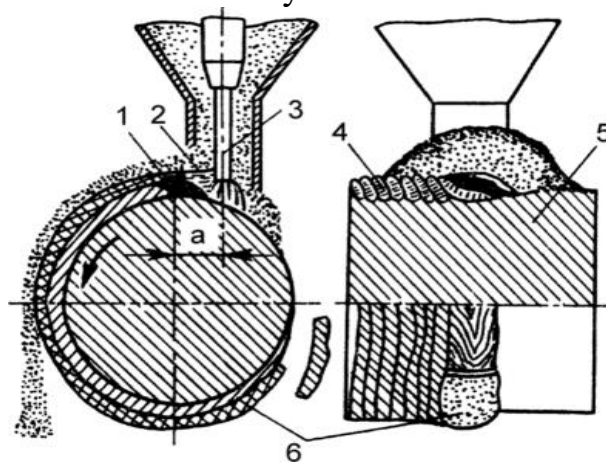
Схема наплавки цилиндрических поверхностей деталей под флюсом
